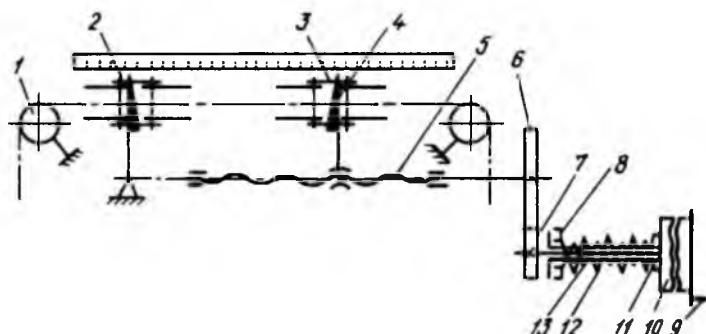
Схема приспособления для контроля втулочно-роликовых цепей:
